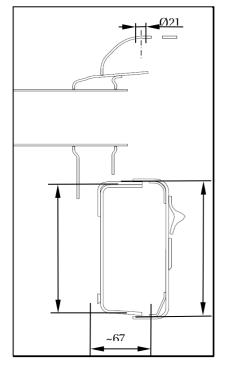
Sezione Q-Q (Amarok SC)
